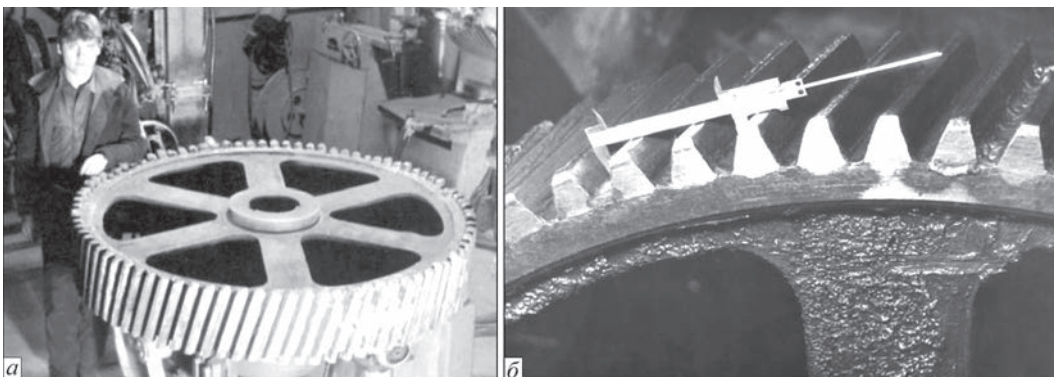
Зовнішній вид відновленого зубчастого колеса після термічної обробки (а) і встановленого в привід обертання окорувального барабана (рис. 8, б) після механічної обробки наплавлених зубів (б)
